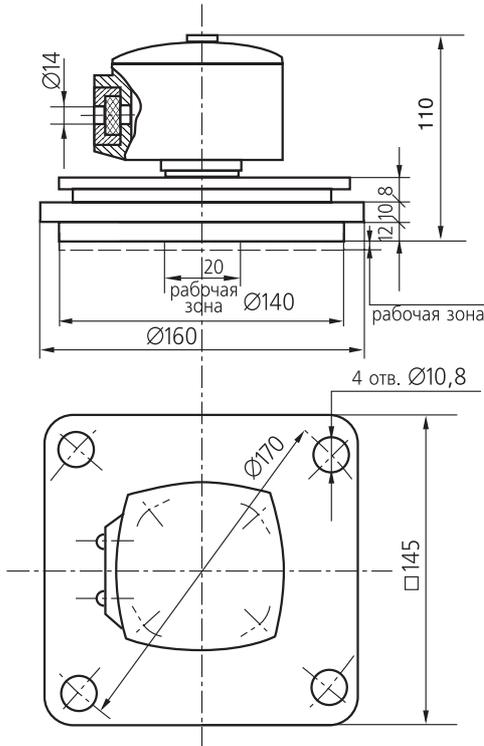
Общий вид, габаритные и установочные размеры СУС 181Р(Б)
